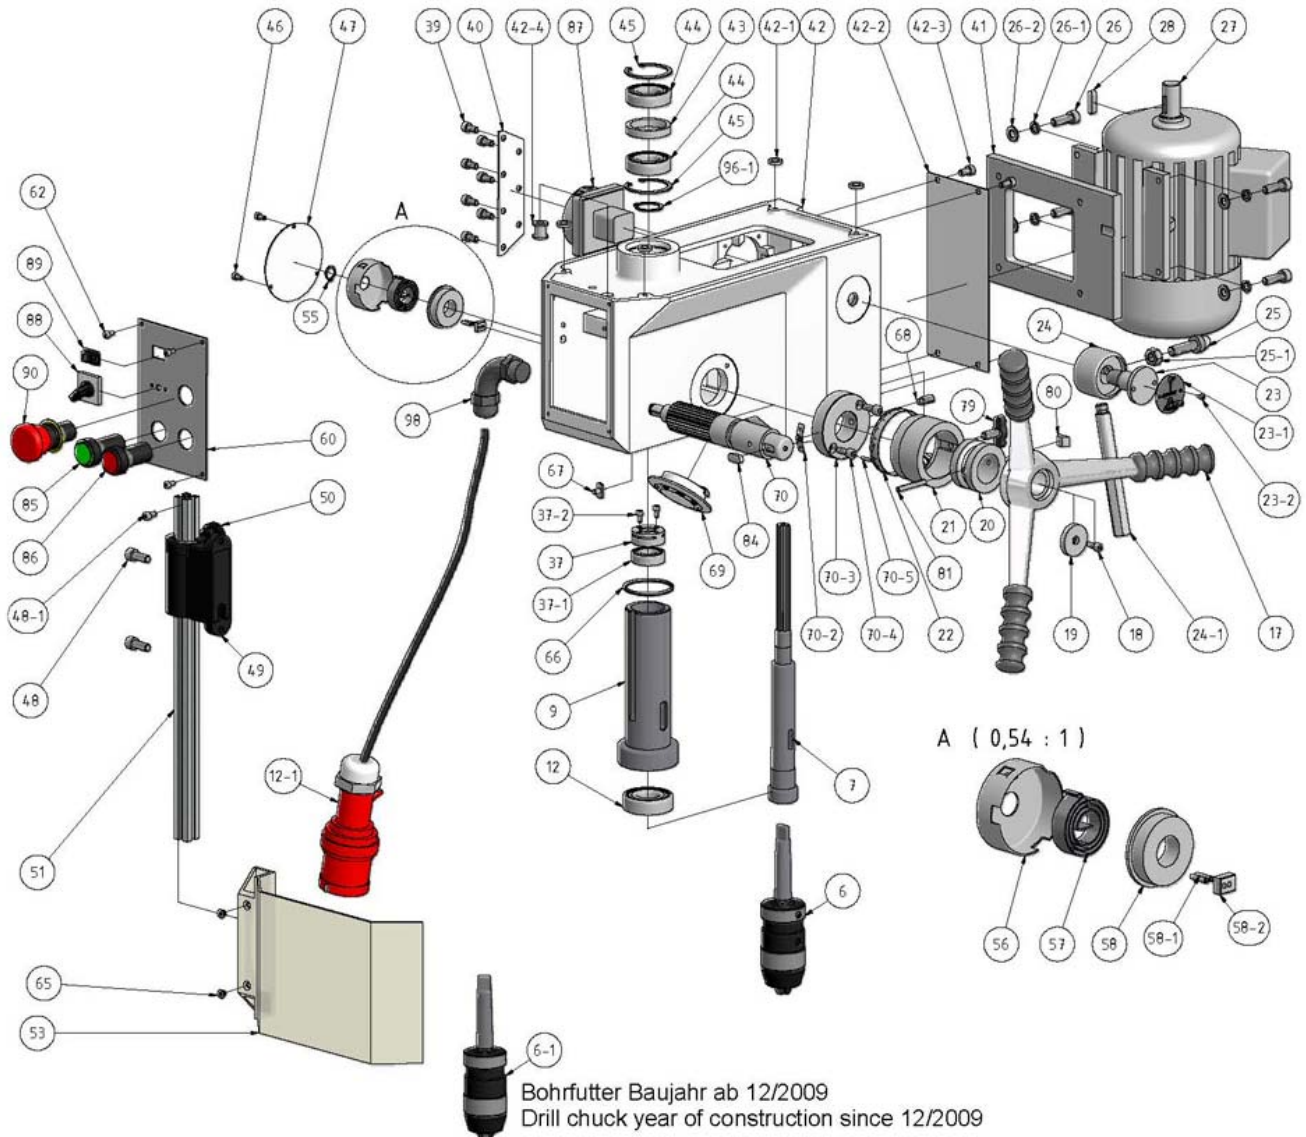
Bohrkopf B24H - Drilling head B24H
